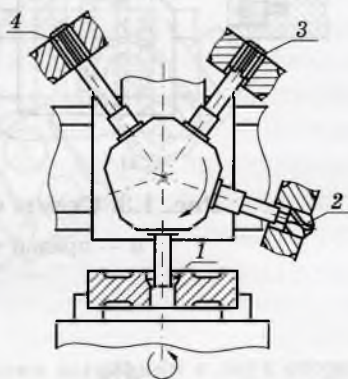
Схема обработки отверстия заготовки зубчатого колеса на токарно-карусельном станке:
